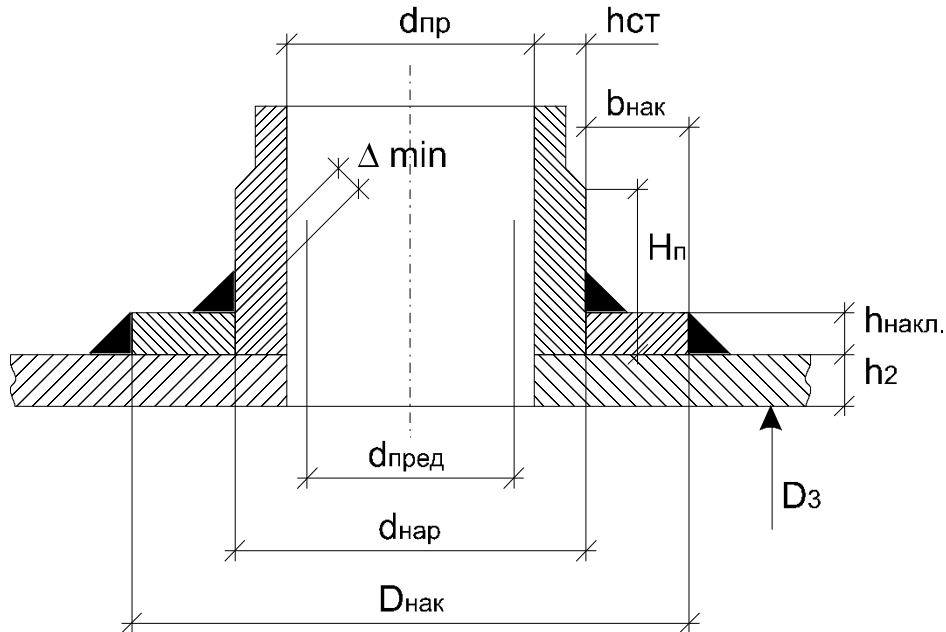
Расчетная схема уКПепления патрубка
